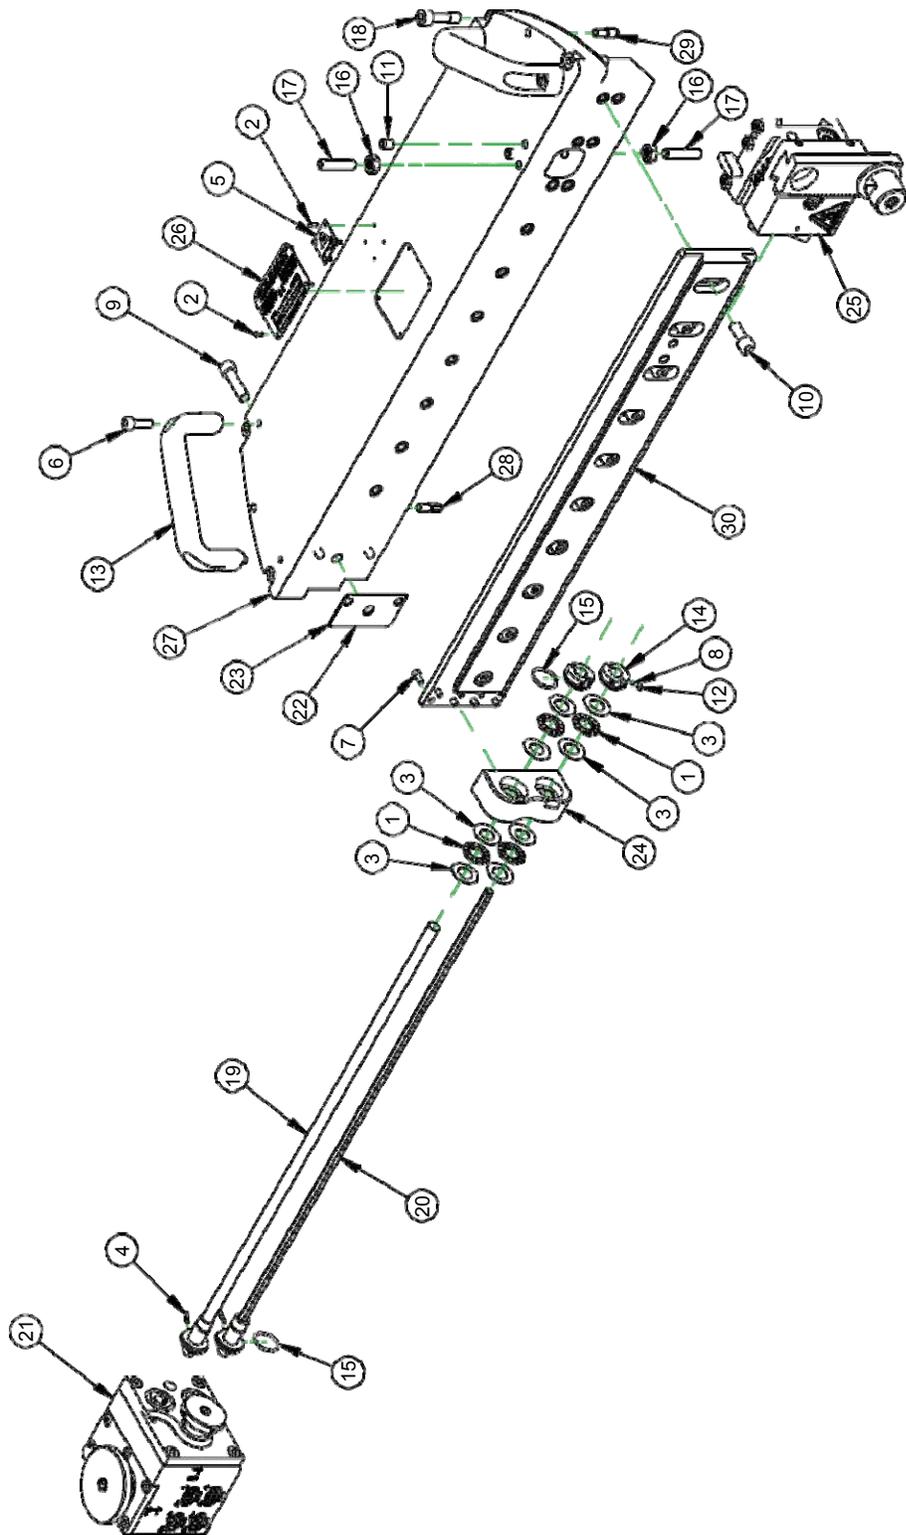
ENSEMBLE DE GLISSIÈRE RADIALE ET AXIALE FF2400 (RÉF. 80683)
